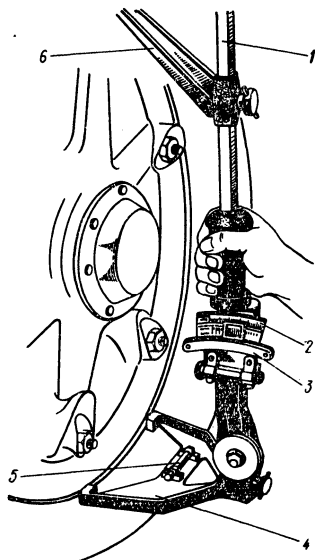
Прибор для проверки углов развала колес и наклона шкворней:
